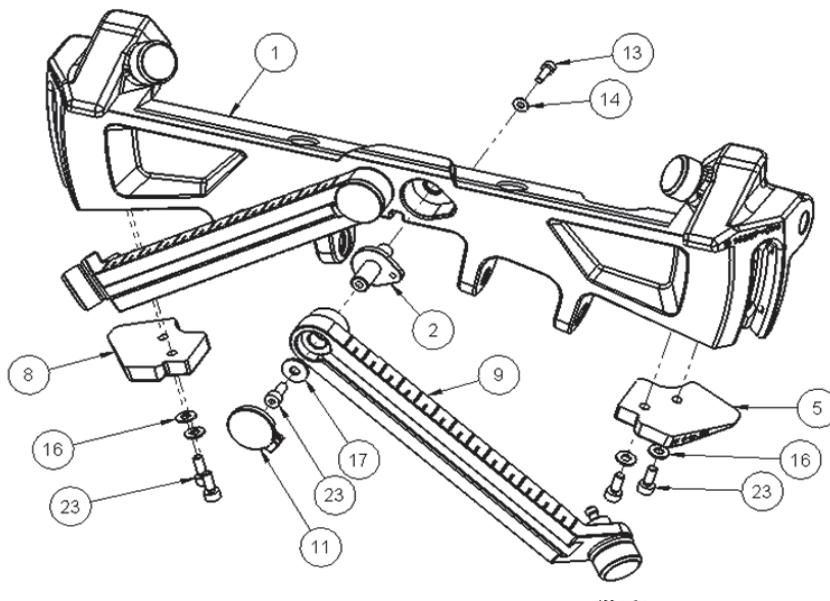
Vista esplosa del gruppo frontale: 1° parte
